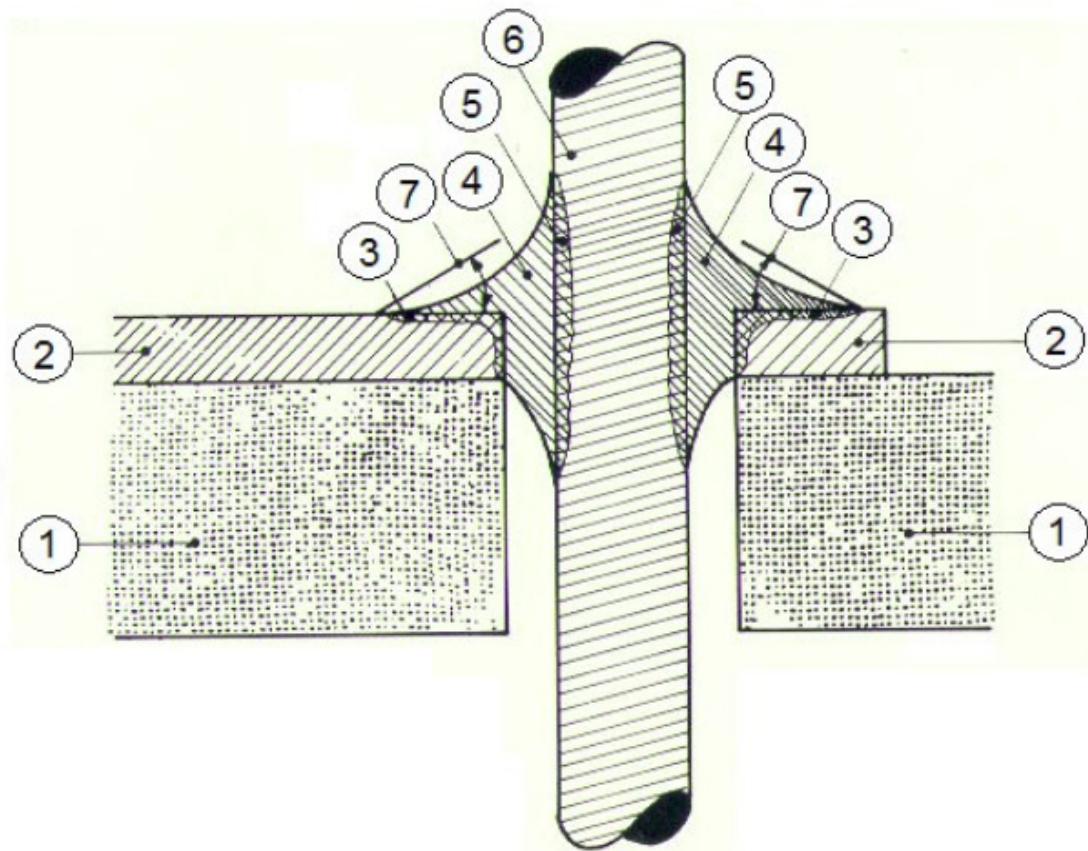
Partes de uma PCI e uma soldagem eficiente.
